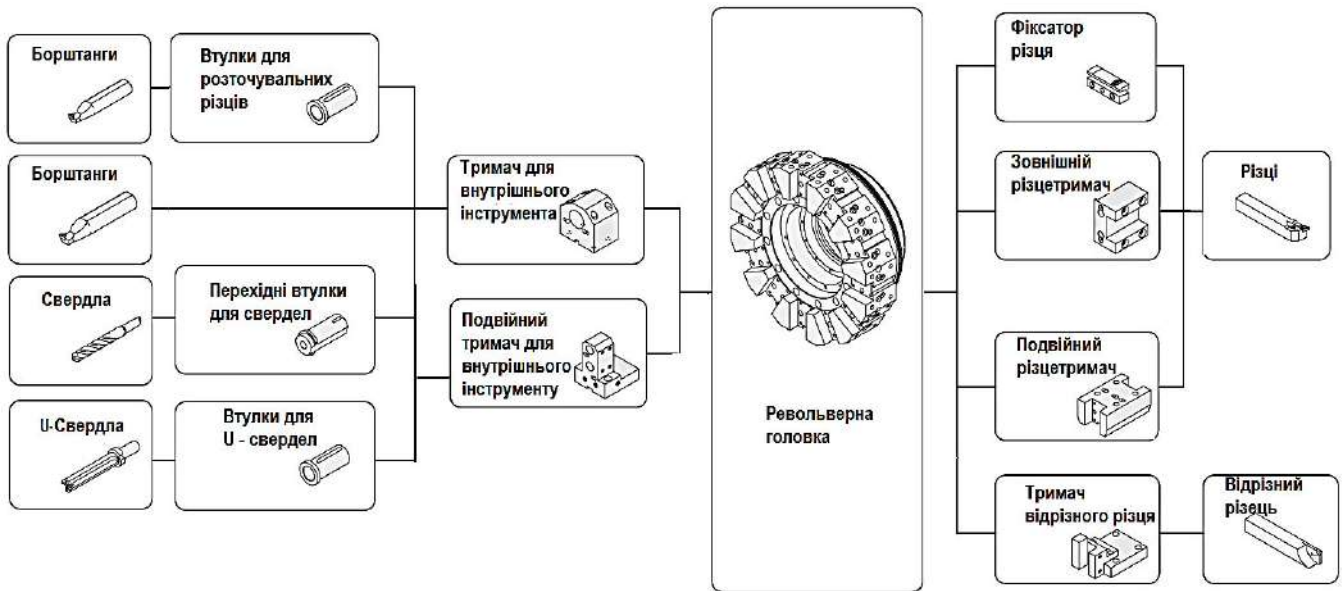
Тримачі інструмента і перехідні втулки для револьверних головок
